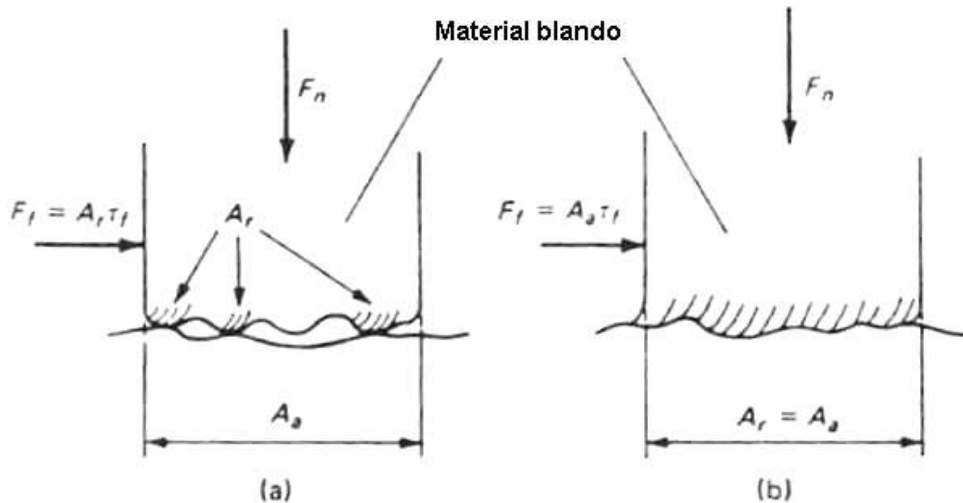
(a) Rozamiento por deslizamiento (b) Rozamiento por soldadura
